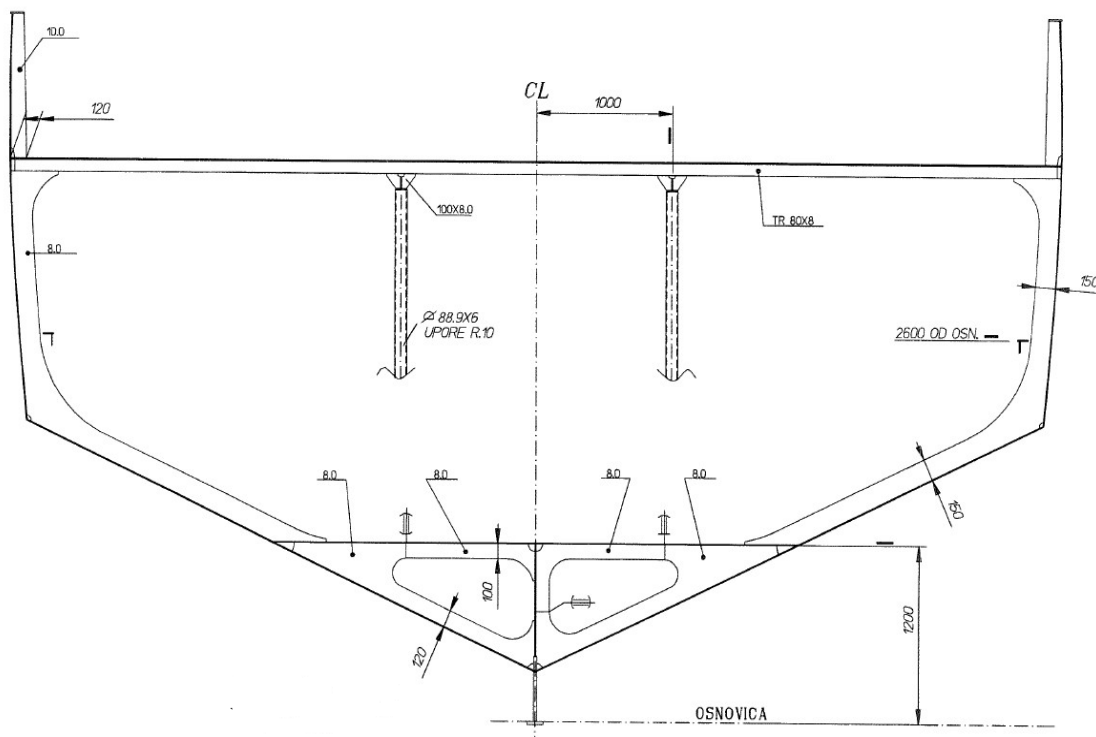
Opći plan konstrukcije broda sa označenim dijelom dvodna sa tankovima (izvor: HRB)
